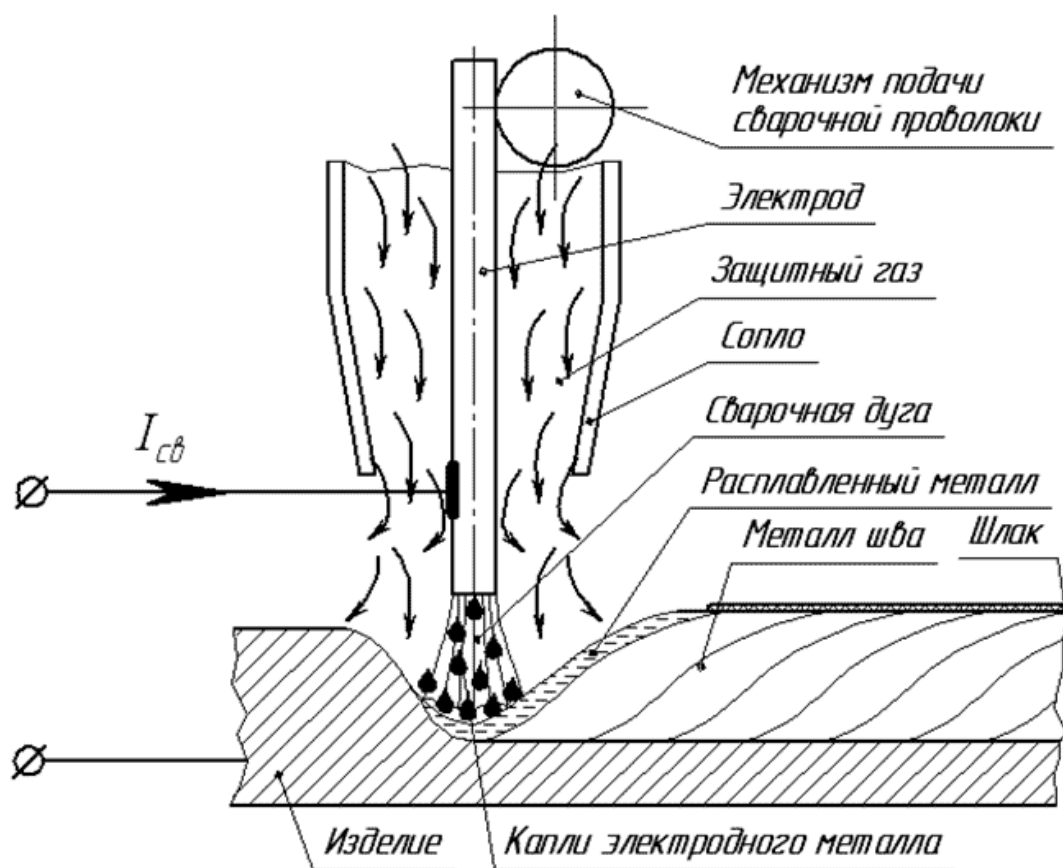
Схема сварочного процесса в среде защитных газов
